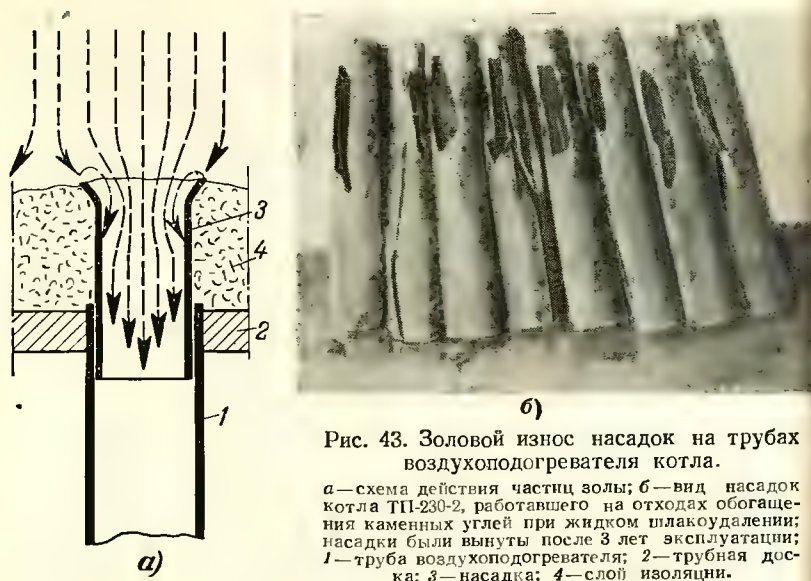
Золовой износ насадок на трубах воздухоподогревателя котла.
